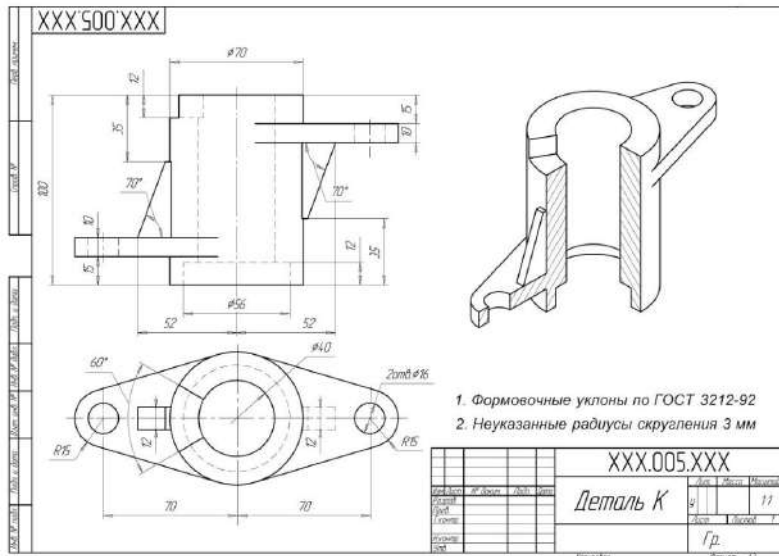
Приклад розміщення ізометричного зображення деталі на робочому кресленні
